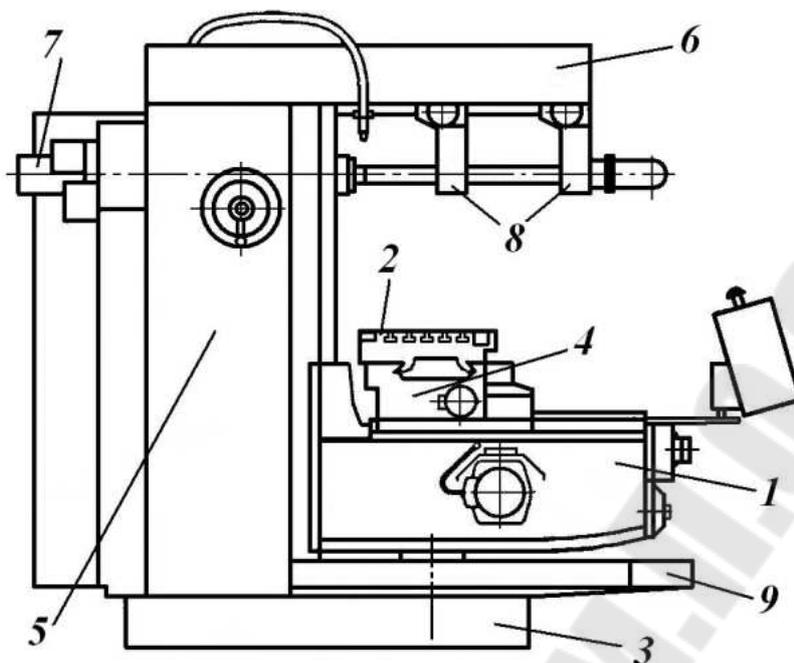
Профильная проекция общего вида горизонтально-фрезерного станка FU450R:
